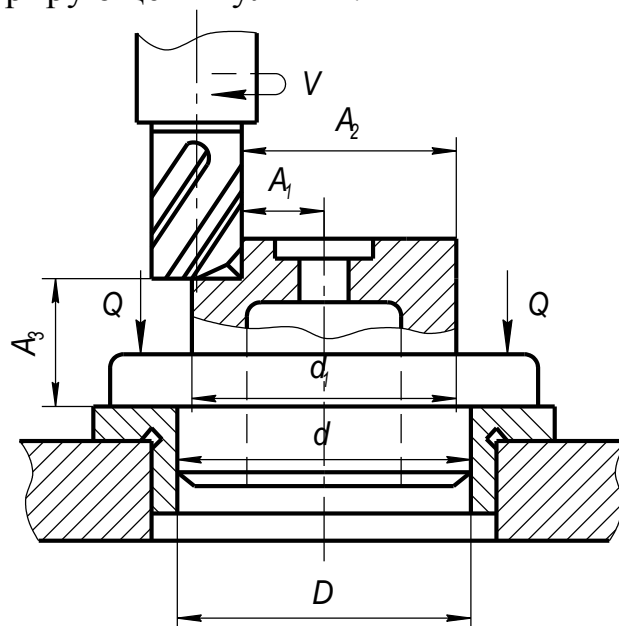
Схема установки заготовки при фрезеровании
